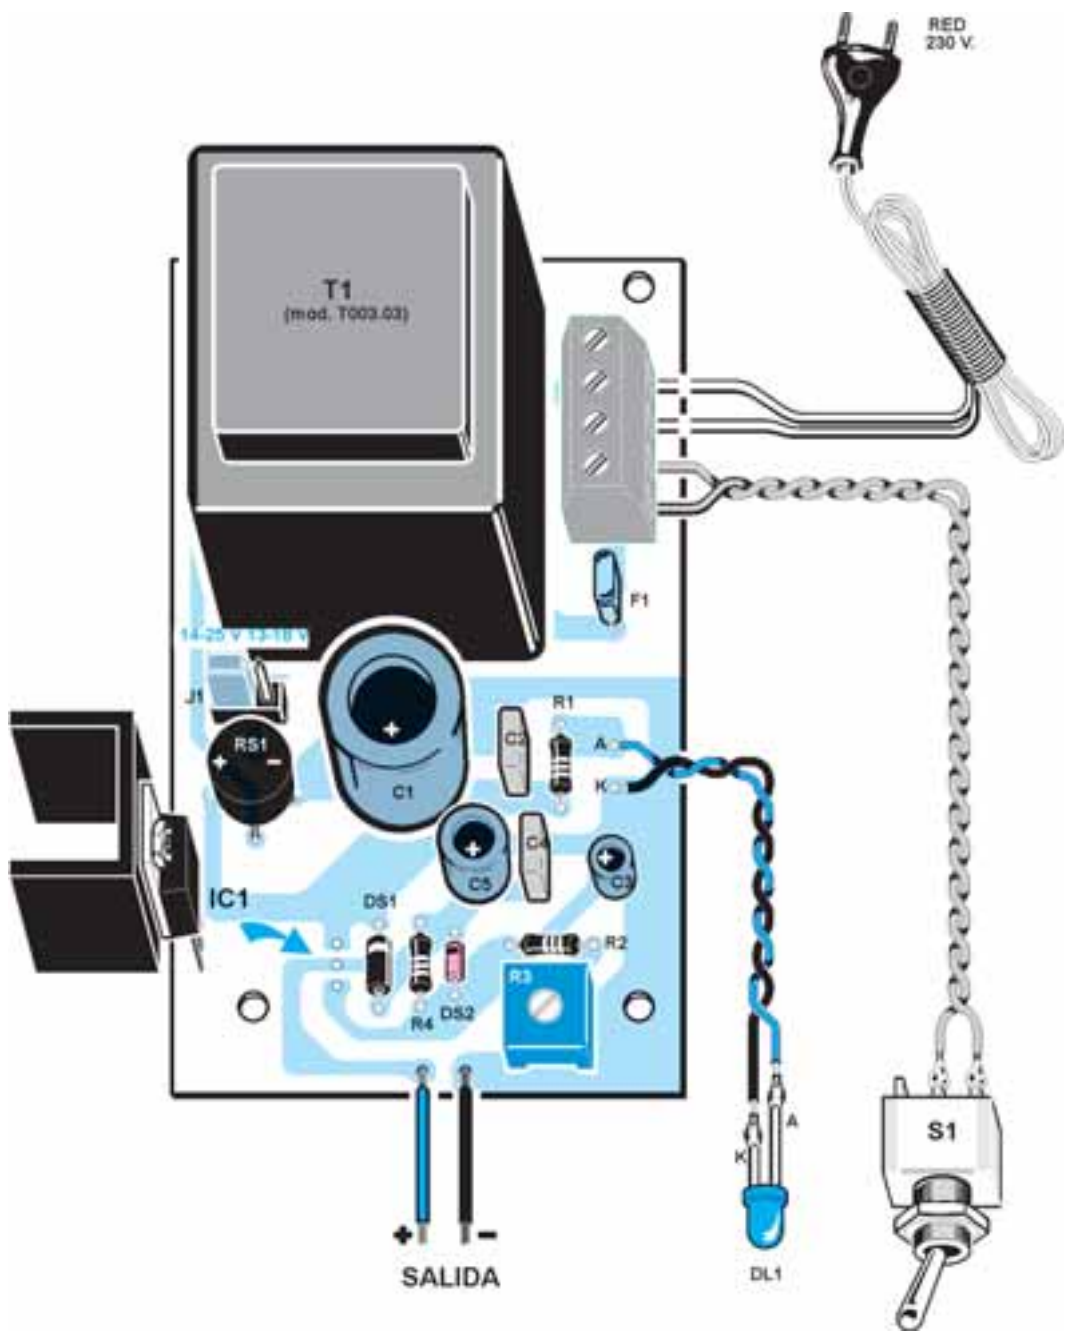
Esquema práctico de montaje del alimentador LX.1174/24. El regulador LM317 debe ser montado en primer lugar en la pequeña aleta de refrigeración y, a continuación, soldado al circuito.
